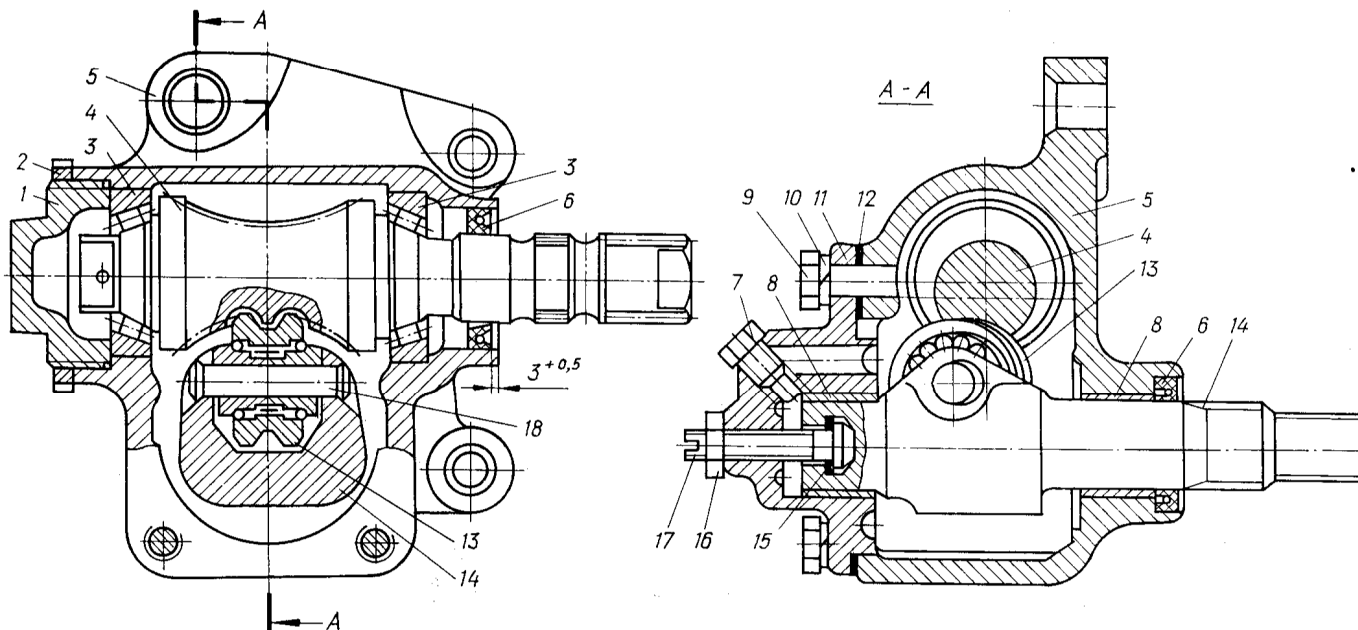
Механизм рулевой (без вала, опоры вала и рулевого колеса):
